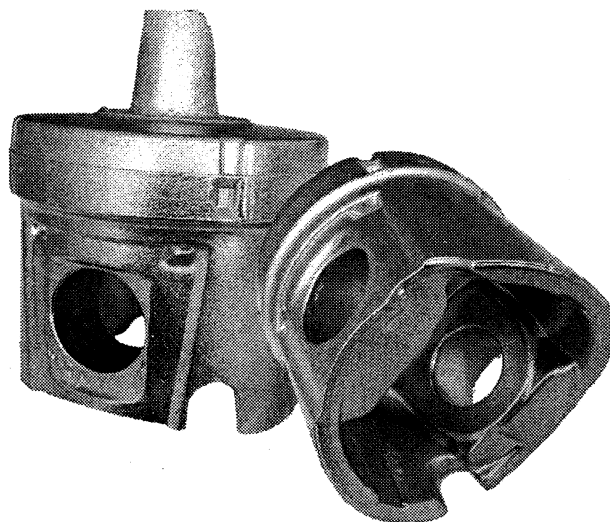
Отливки поршней, изготовленных на оборудовании НП РУП «Институт БелНИИлит»
